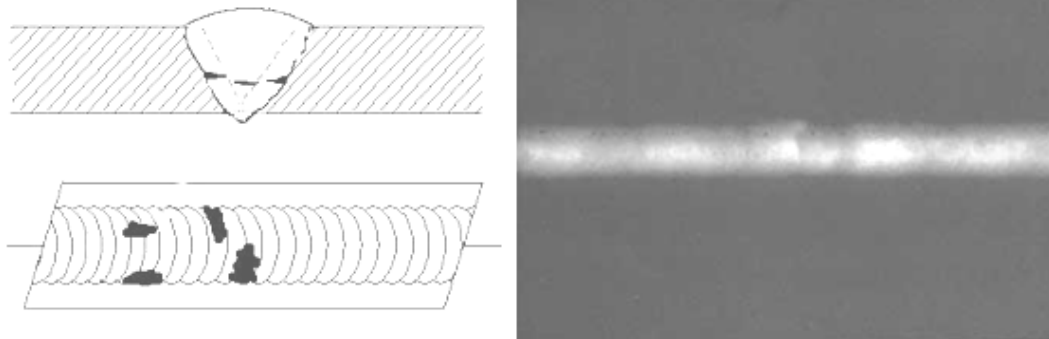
Soldadura Fría (Cold Lap).
